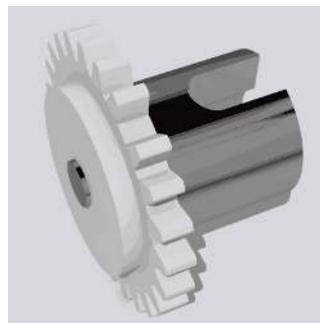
基于 Shapr3D 实现的液压弹簧断路器齿轮连接固定装置 3D 建模图
